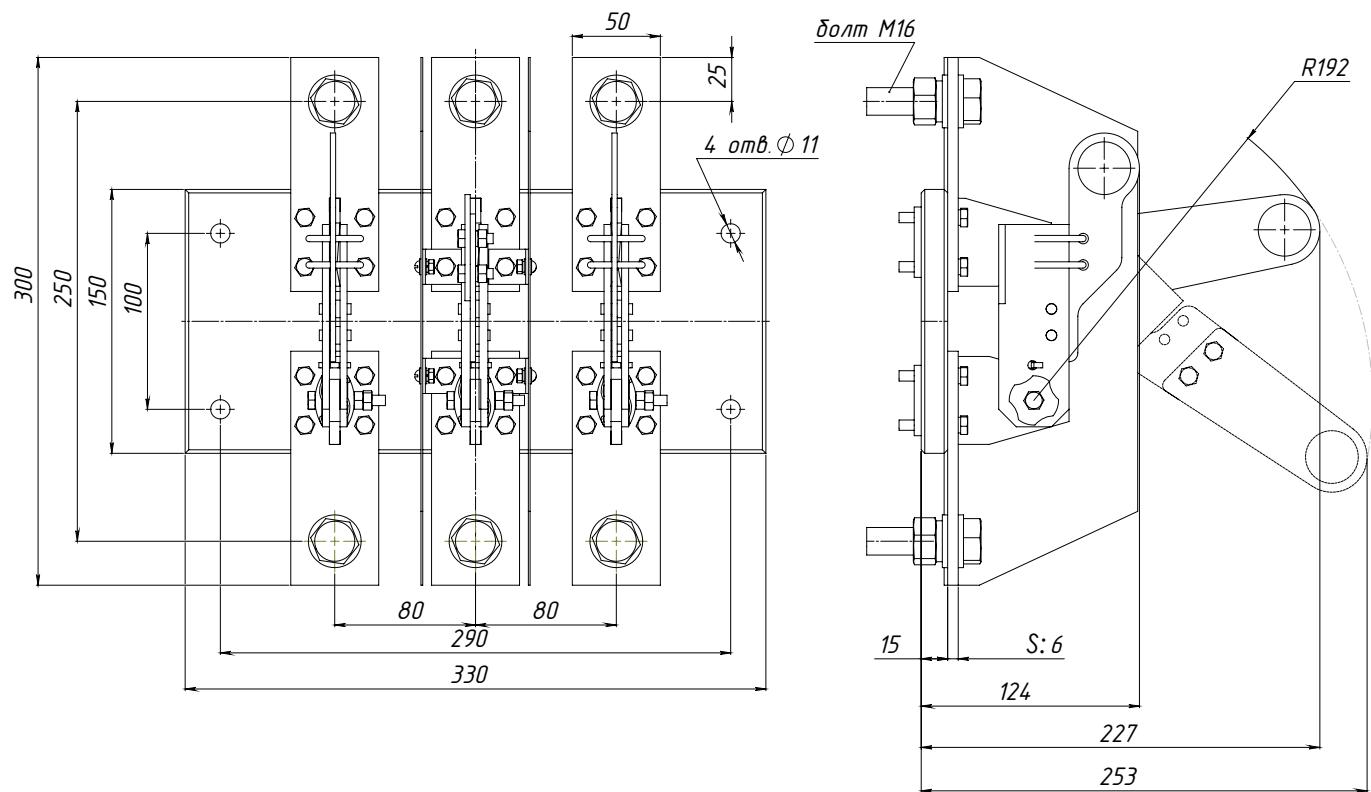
Разъединитель Р103 с пополюсным оперированием штангой ШО-1 на номинальный ток 1000 А
